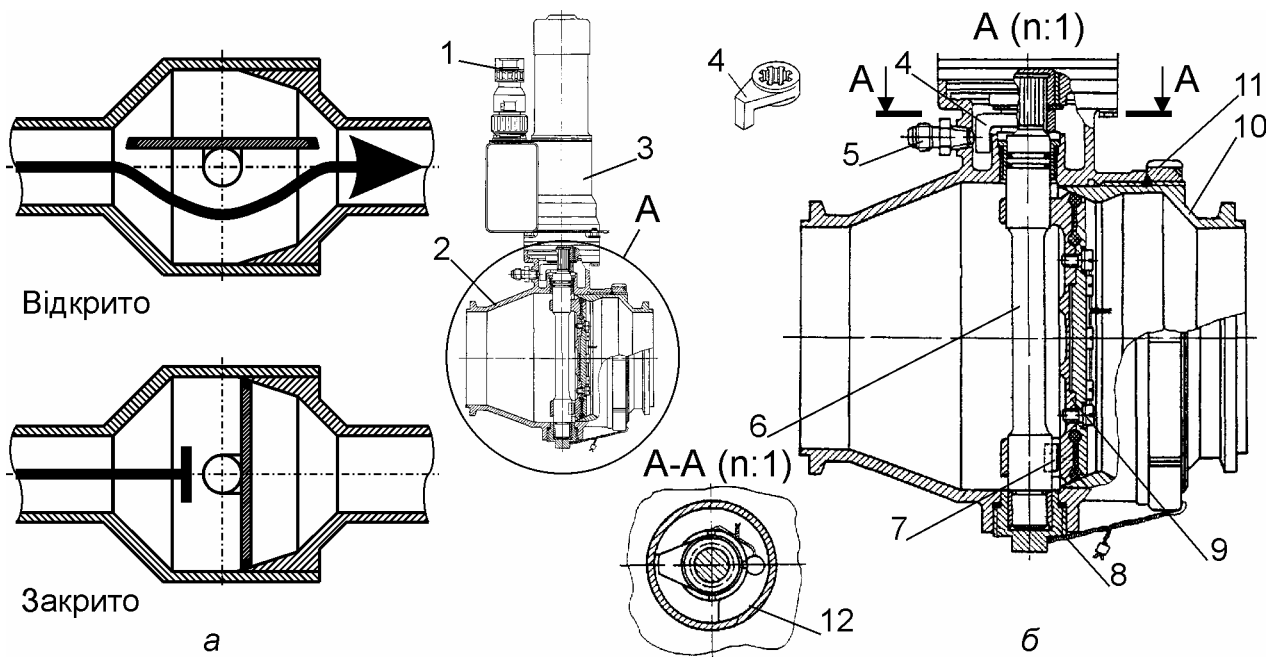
Заслінковий кран (Ан-124): а — схема роботи; б — конструкція; 1 — електрорознім; 2 — корпус крана; 3 — електромеханізм; 4 — упор на валу; 5 — дренажний штуцер; 6 — вал; 7 — шпонка; 8 — підшипник; 9 — заслінка; 10 — фланець; 11 — гайка; 12 — упор на корпусі
